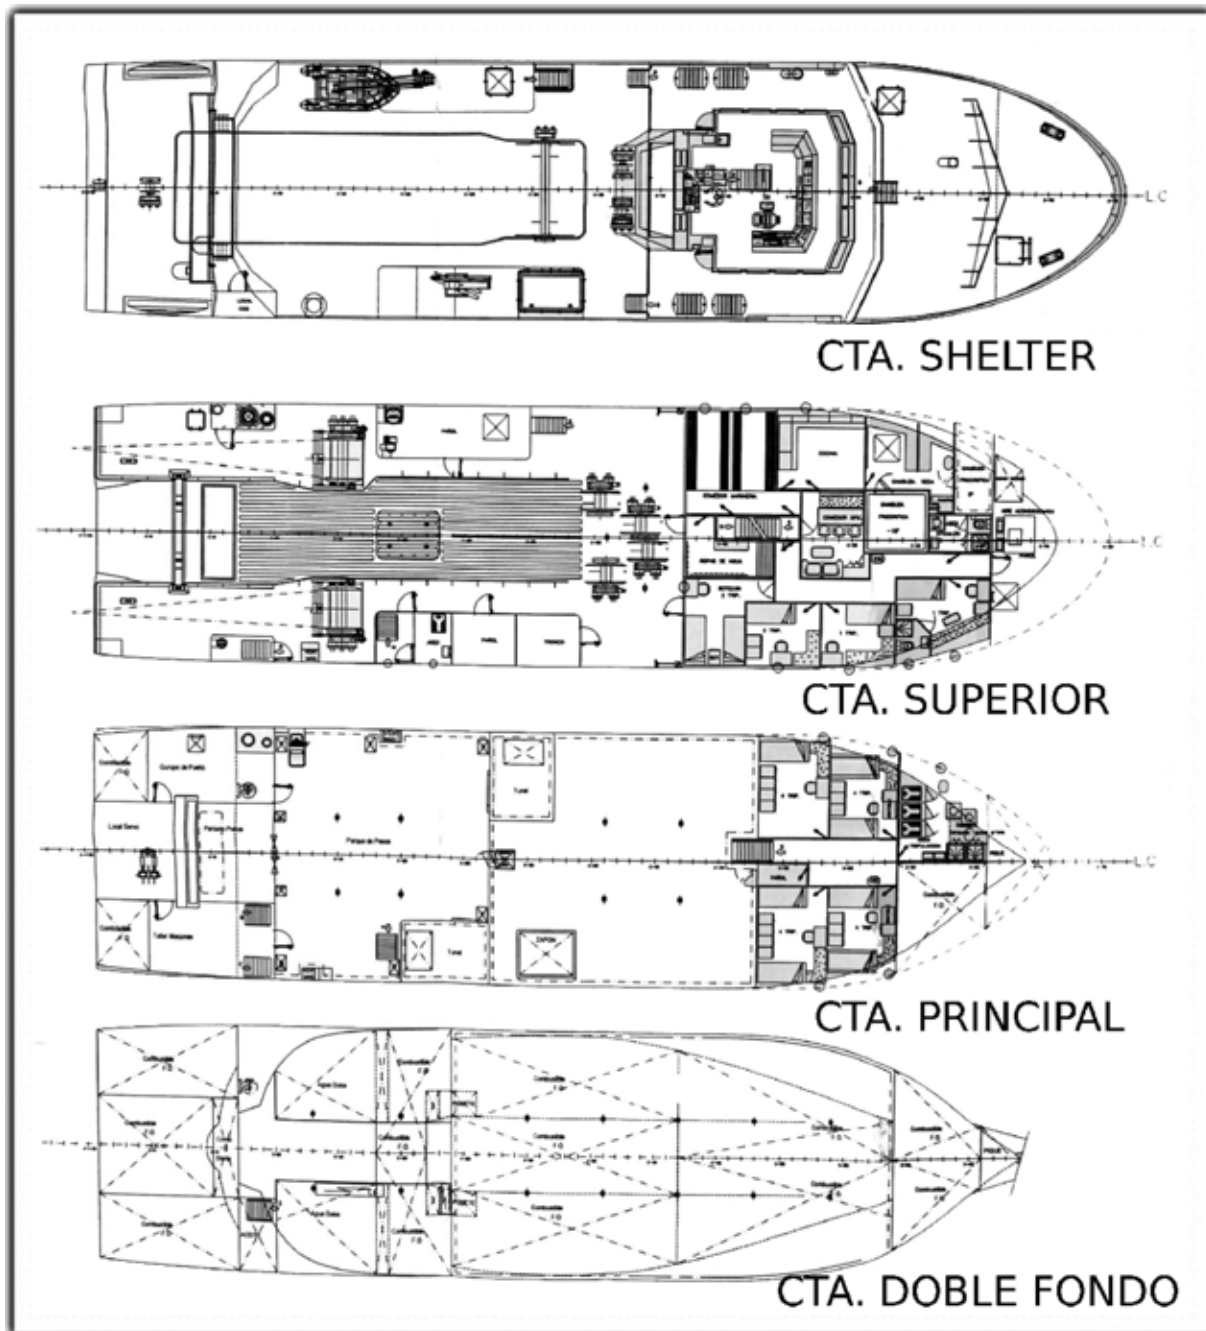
Plano de las cubiertas de B/P MONTE GALIÑEIRO
